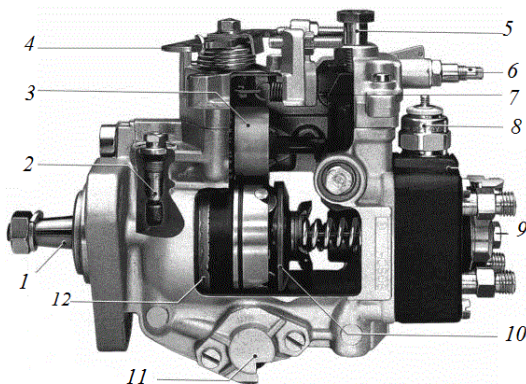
Топливный насос: 1 – вал привода насоса; 2 – перепускной клапан регулирования внутреннего давления; 3 – рычаг управления подачей топлива; 4 – грузы регулятора; 5 – жиклер слива топлива; 6 – винт регулировки полной нагрузки; 7 – передаточный рычаг регулятора; 8 – электромагнитный клапан останова двигателя; 9 – центральная пробка; 10 – кулачковый диск; 11 – автомат опережения впрыска топлива; 12 – топливоподкачивающий насос низкого давления
